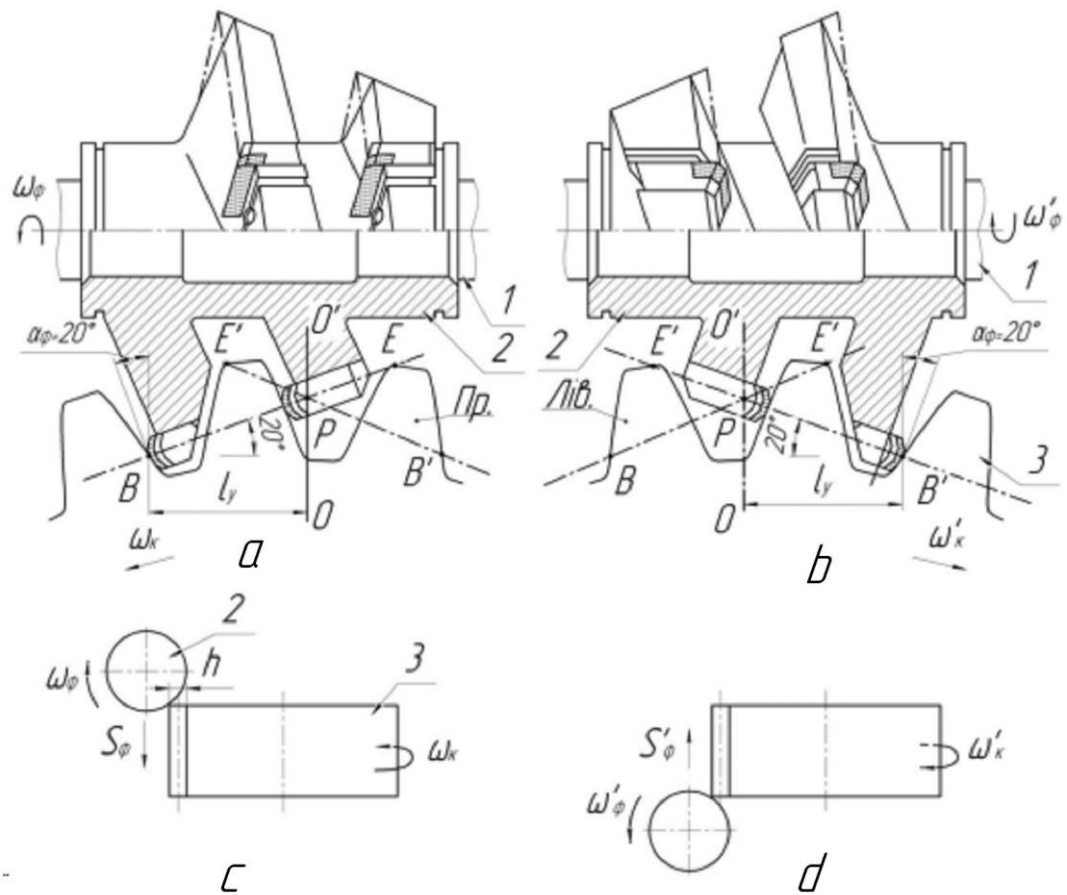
Схема оброблення зубів колеса одним правим корпусом фрези: *a, c* – правий корпус при зустрічному фрезеруванні; *b, d* - правий корпус при попутному фрезеруванні з реверсивним напрямком обертання фрези та нарізаного зубчастого колеса
